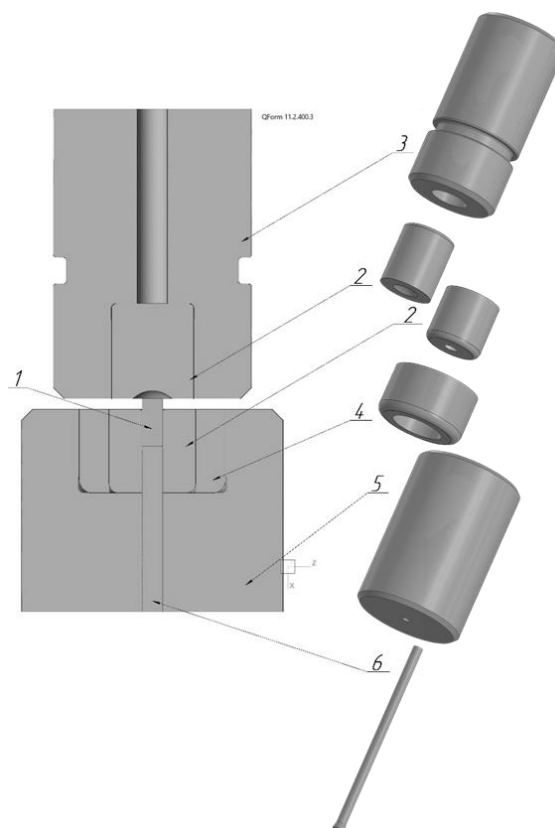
Схема формообразующего инструмента для высадки заклепок
